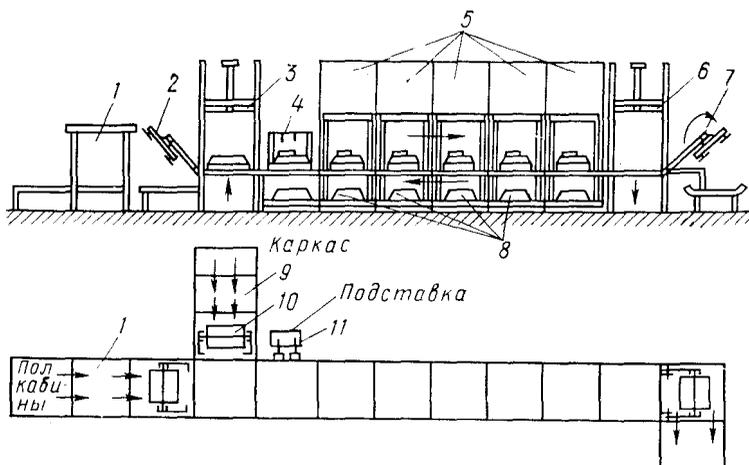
Схема автоматической линии сборки и сварки настила пола кабины грузового автомобиля
